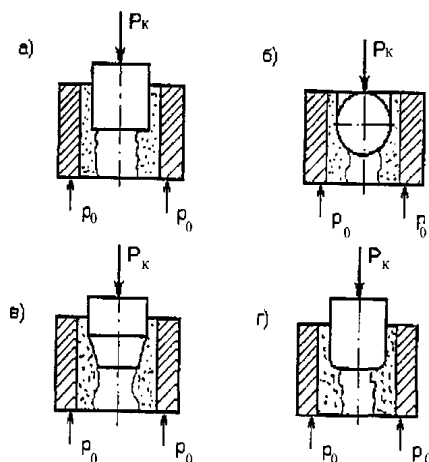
Схема динамічного формування шару композиції шляхом використання калібрів (P_k - сила калібрування, P_o - опорна реакція): а – циліндричним калібром; б – сферичним калібром; в – циліндричним калібром з конусною фаскою; г – циліндричним калібром з сферичною фаскою.
